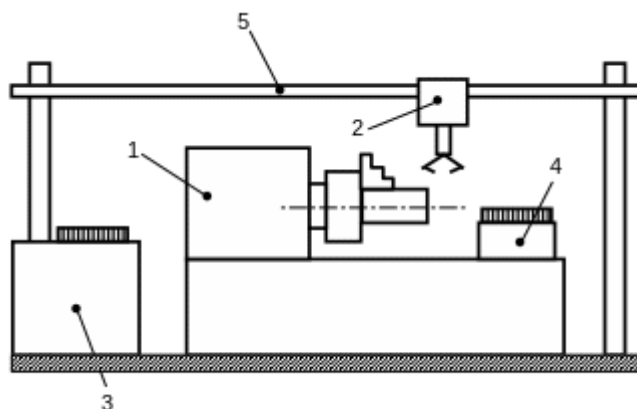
Схема ГПМ с подвесным транспортным роботом: 1 – станок мод. 16К20Ф3; 2 – подвесной транспортный робот; 3 – накопитель заготовок и деталей; 4 – инструментальный магазин; 5 – подвесная транспортная линия
